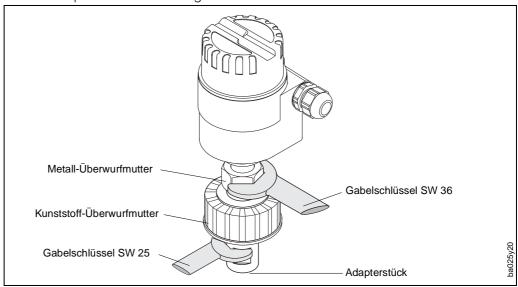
Montage des Adapterstücks für Kunststoffrohrleitungen
